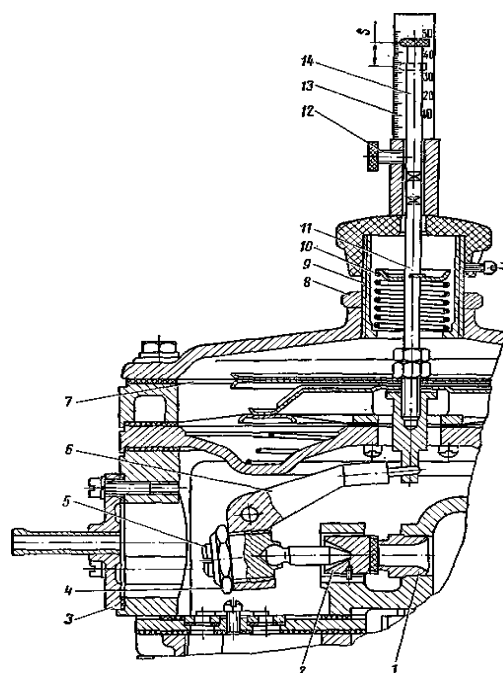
Приспособление для замера хода клапана второй ступени редуктора МКЗ-НАМИ:
